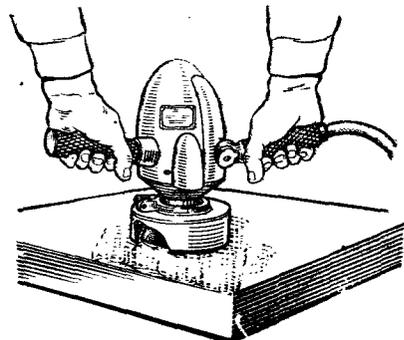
Прием шлифования поверхностей торцовой поверхностью абразивного круга вертикальной пневматической машинкой
